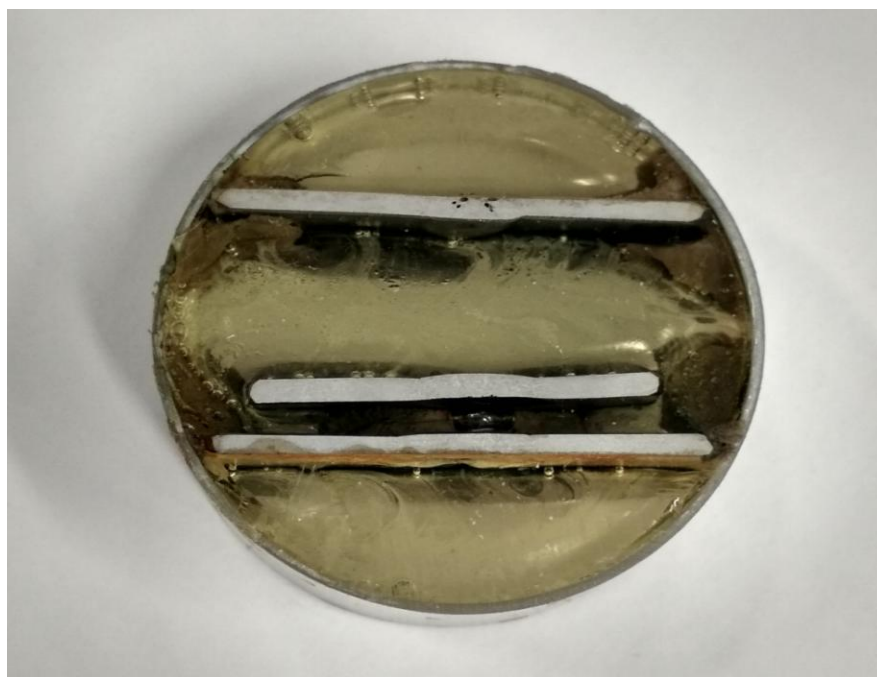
Общий вид приспособления для шлифования образцов
